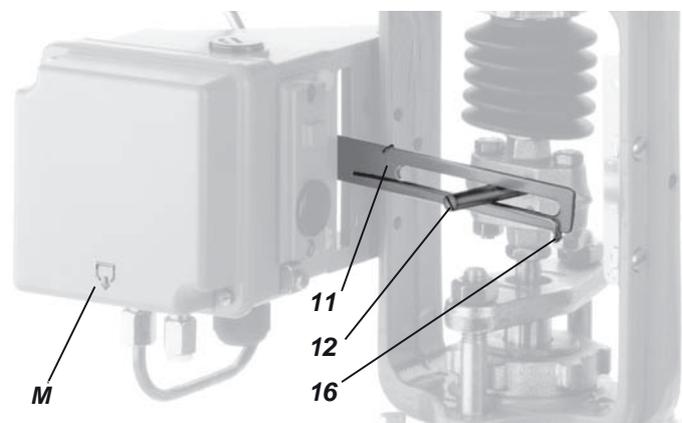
Ponto de partida do posicionador (montagem no lado esquerdo)
